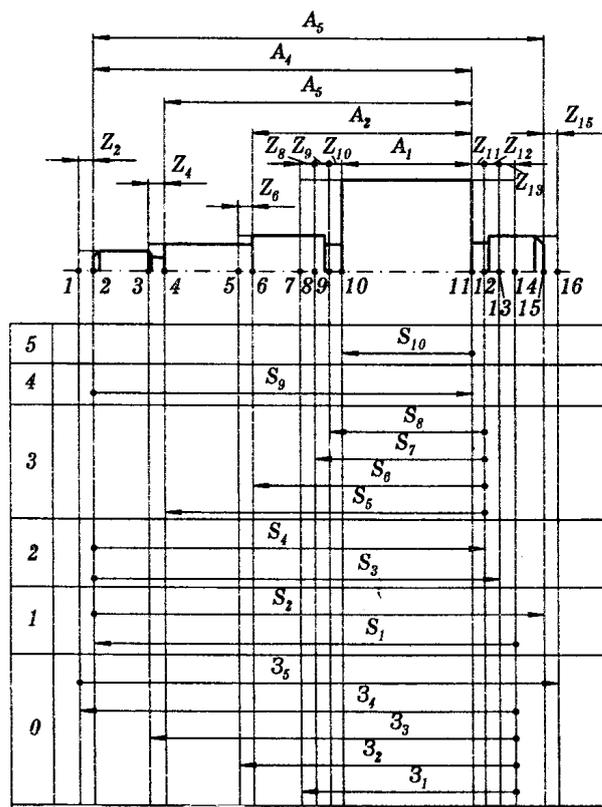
Размерная схема технологического процесса обработки торцевых поверхностей вала-шестерни [2]: A – конструкторские размеры, Z – величины припусков, Z – размеры заготовок, S – технологические размеры
